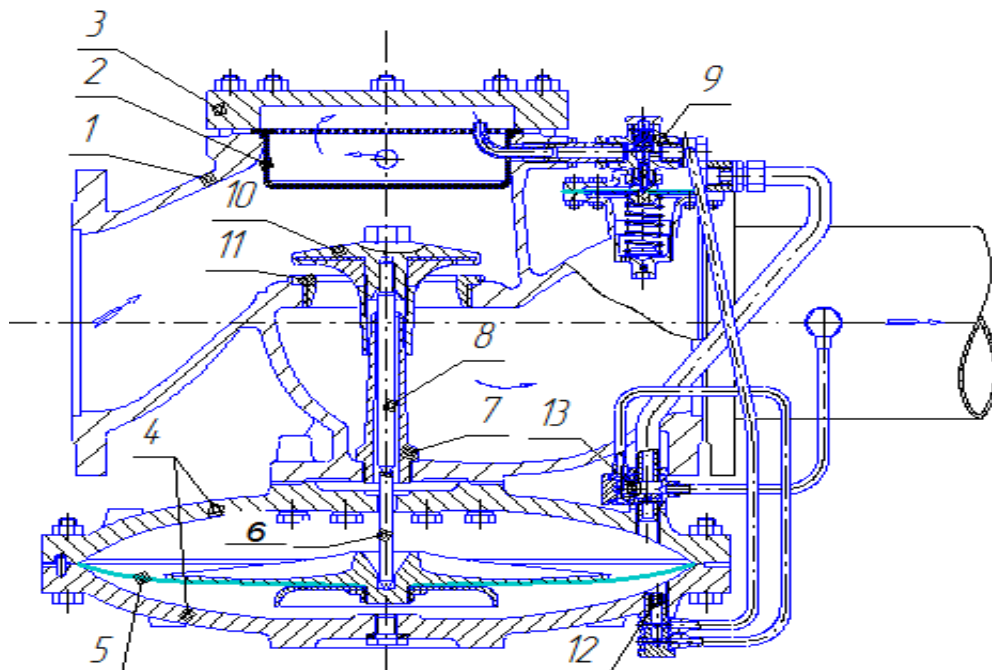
Регулятор давления газа РДУК2: 1 – корпус; 2 – фильтр; 3 – крышка корпуса; 4 – крышки мембраны; 5 – мембрана; 6 – толкатель; 7 – колонка; 8 – шток клапана; 9 – регулятор управления; 10 – клапан регулирующий; 11 – седло; 12 – демпфирующий дроссель $\text{Ø} 1,5 \text{ мм}$; 13 – сбросной дроссель $\text{Ø} 2 \text{ мм}$
